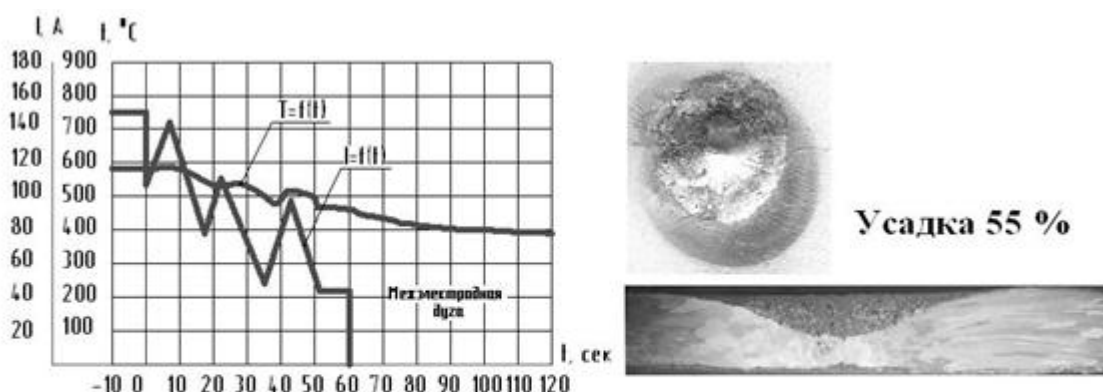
Термический цикл, форма и размеры усадочного кратера при реализации пилообразной формы кривой спада тока сварки
